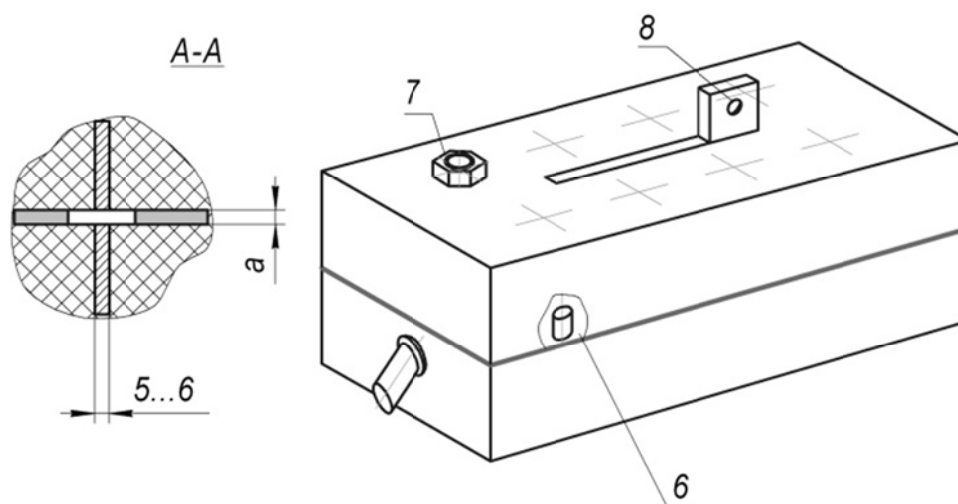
Ячейка длиномерным проточным каналом: 6 – штифты; 7 – крепежное соединение; 8 – токоподводы
